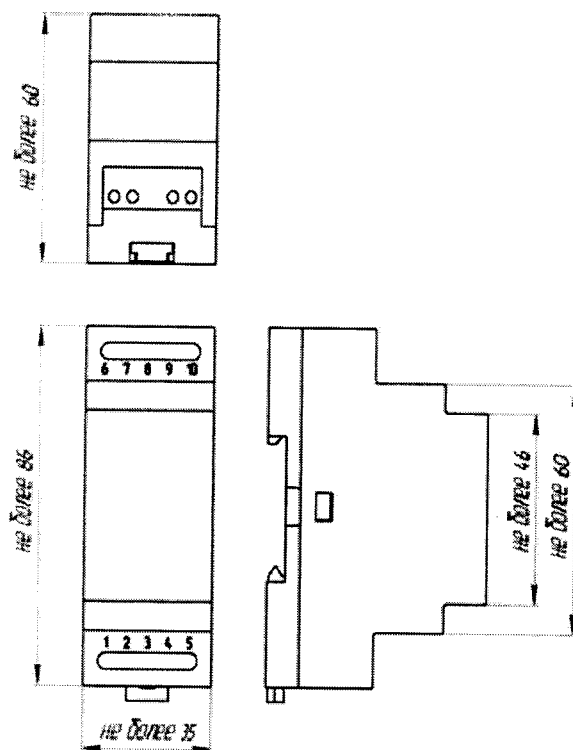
Корпус Д для крепления на DIN-рейку. Степень защиты IP20.
